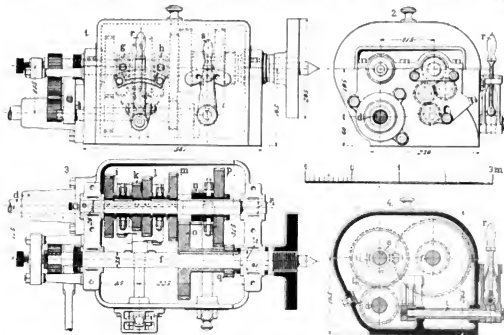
Z. A.: Spindelstock mit Zahnrad-Wechselgetriebe.
